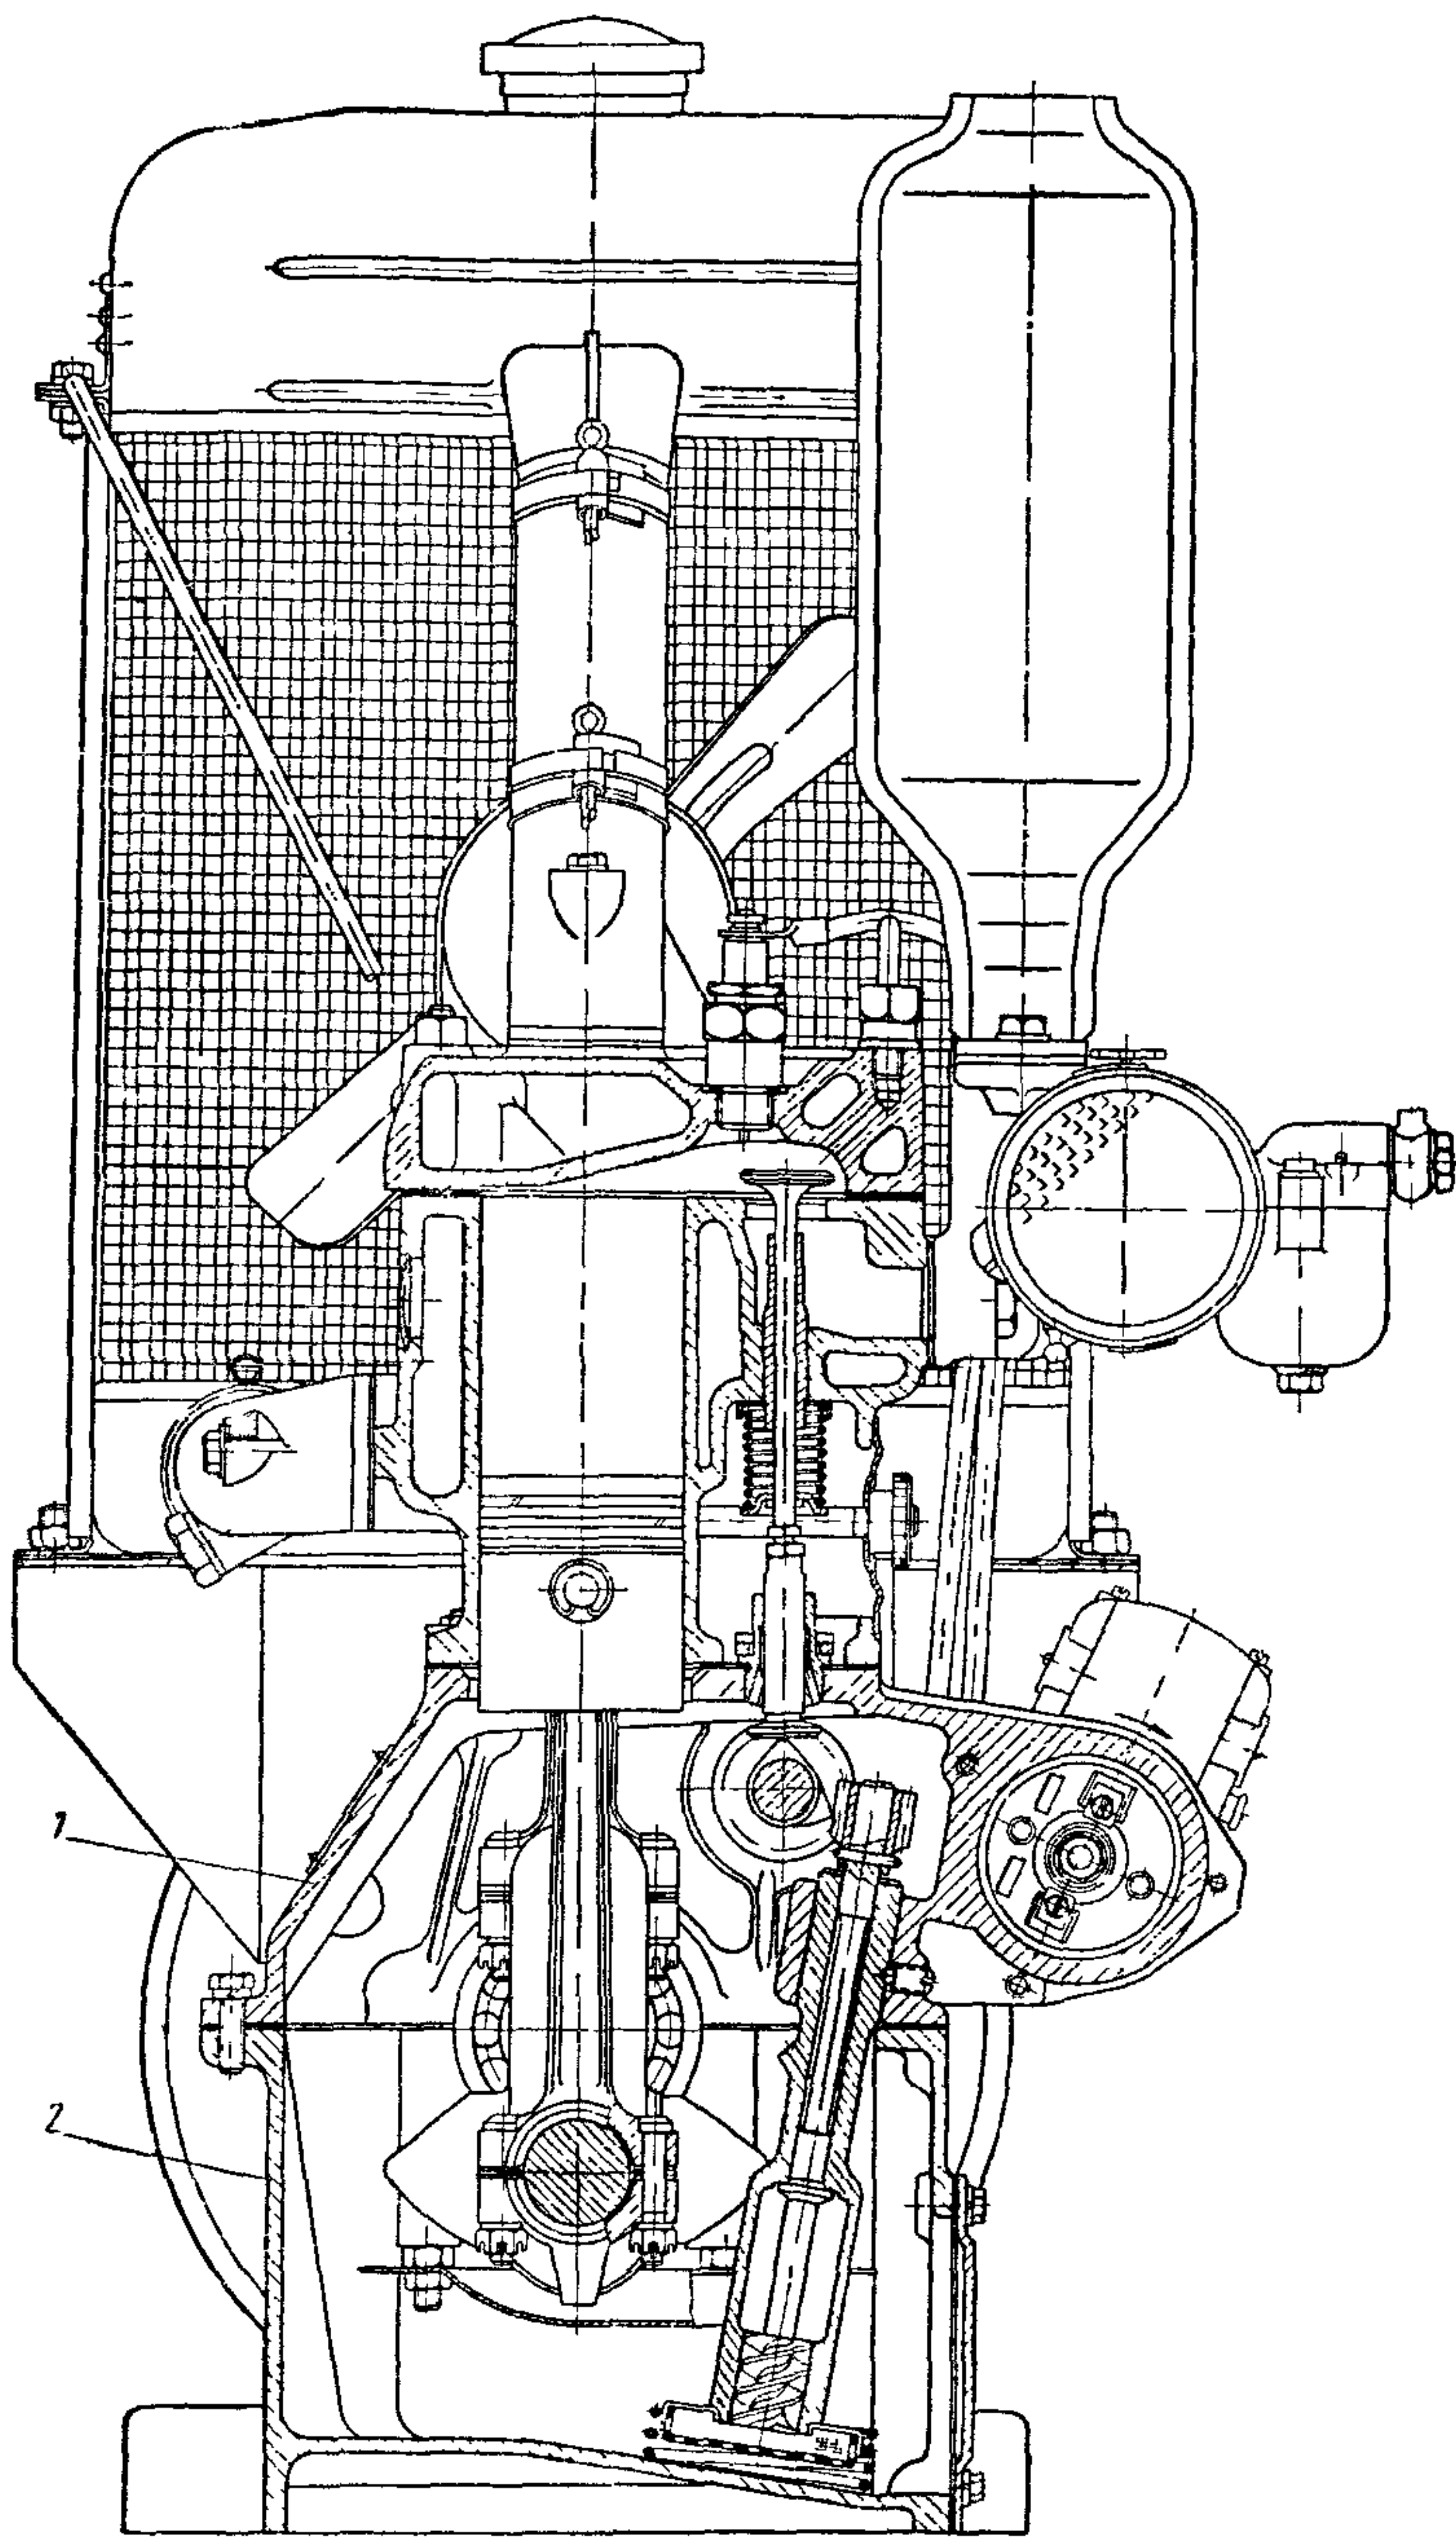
Двигатель Л-3/2, частичный поперечный разрез по оси распределительного вала:
